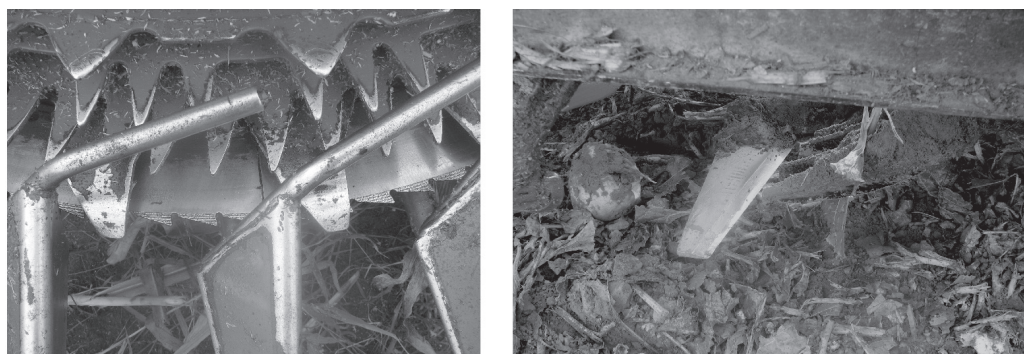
Детали рабочих органов почвообрабатывающих, посевных и кормоуборочных машин
